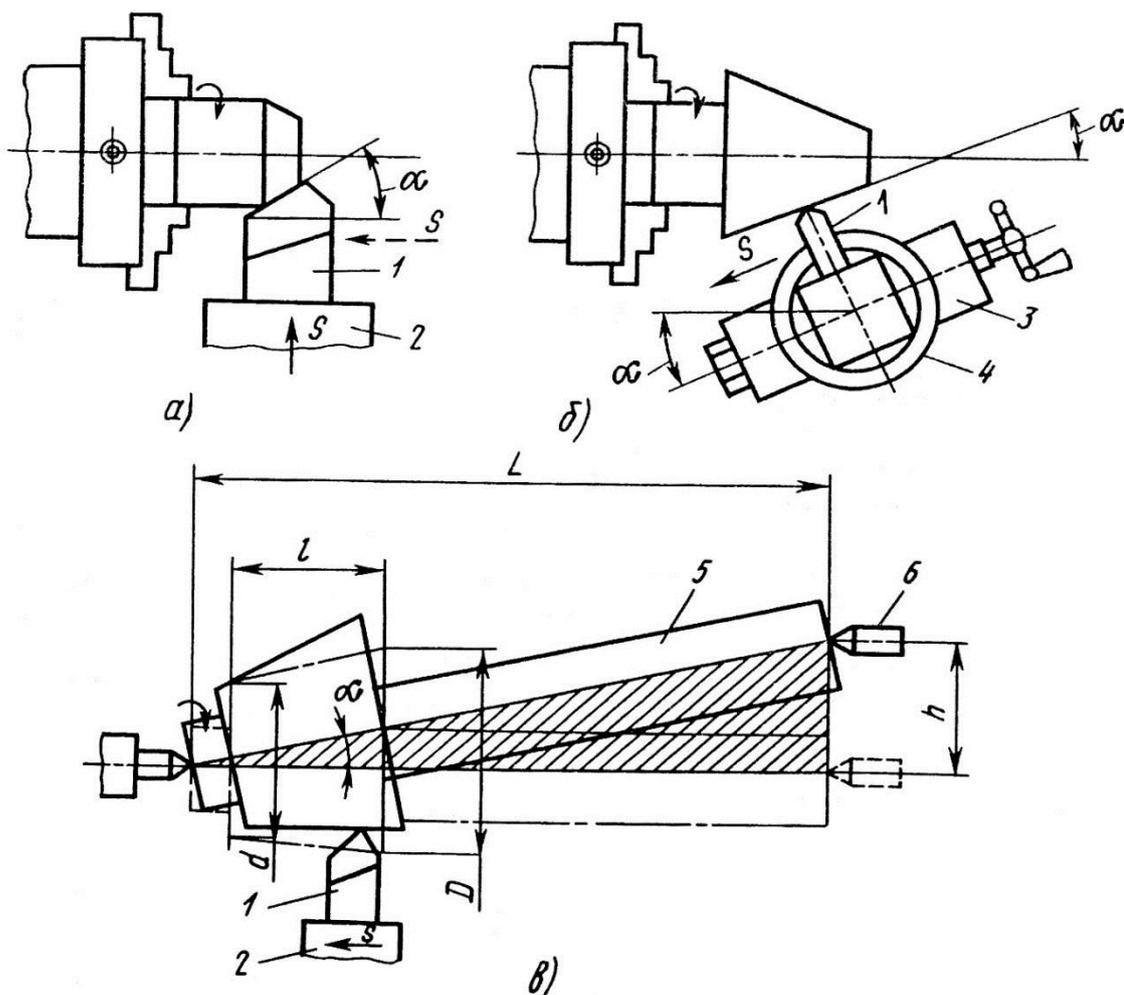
Схемы обработки конических поверхностей на токарно-винторезных станках: а – широким резцом; б – поворотом резцовых салазок; в – смещением корпуса задней бабки.
